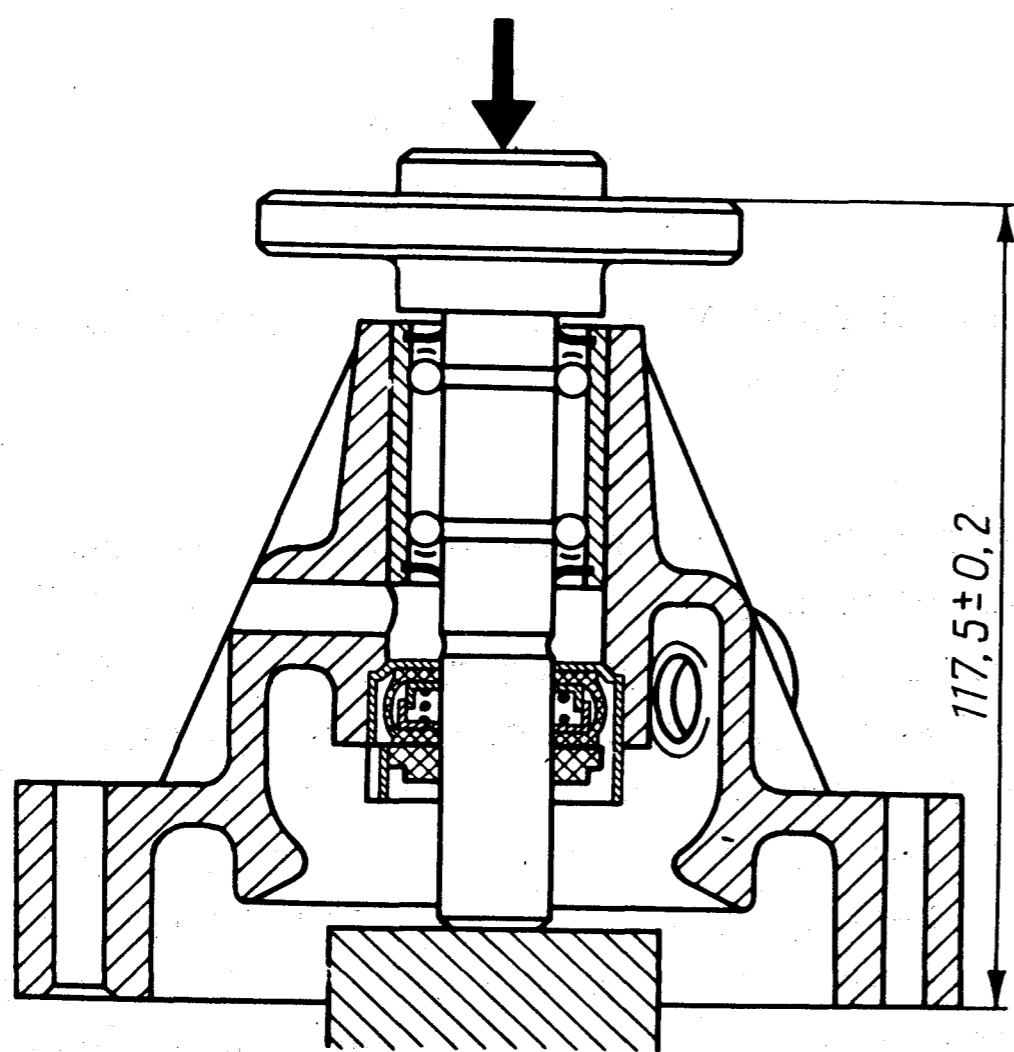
Напрессовка ступицы шкива водяного насоса на вал
